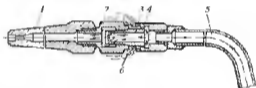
Наконечник с подогревателем для сварки на пропан-бутане:
